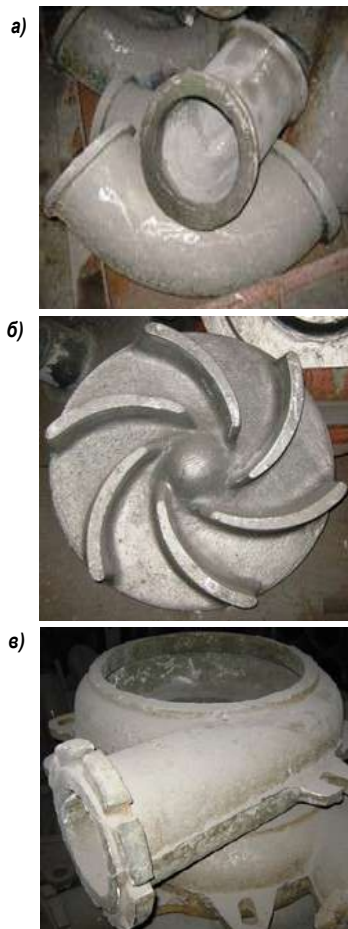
Отливки отливаемые на ПО НМЗ из сплава 280X29НЛ: а – отвод, 8 кг; б – колесо рабочее, 26 кг; в – корпус насоса, 70 кг
